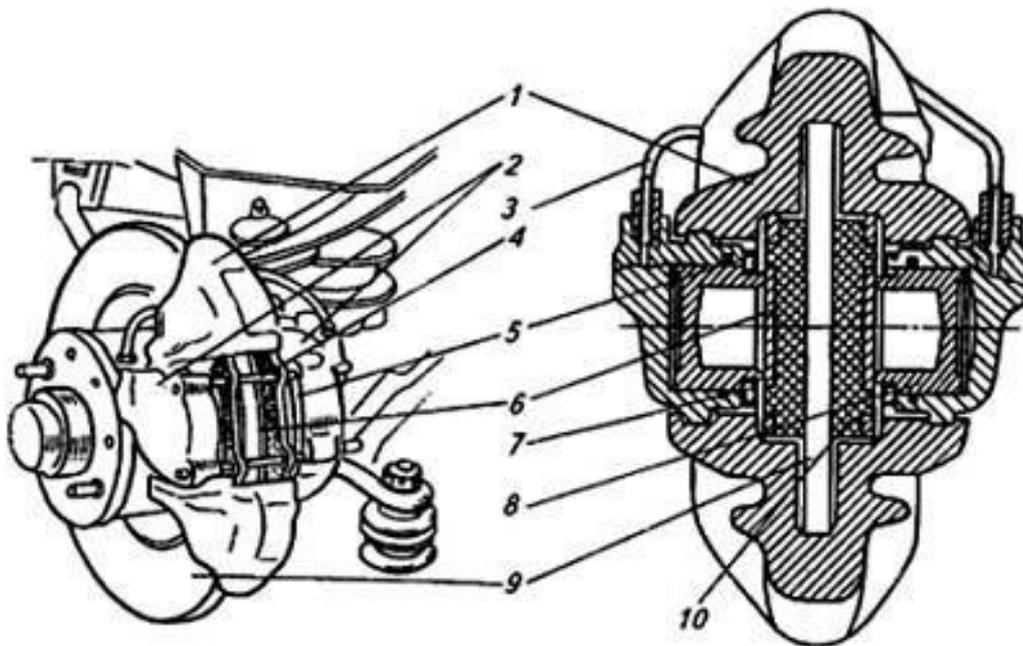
Дисковий гальмівний механізм з фіксованою скобою 1–скоба; 2–гальмівні циліндри; 3–трубопровід; 4–палець; 5–захисний чохол; 6–гальмівна колодка; 7–кільце ущільнювача; 8–поршень; 9–диск; 10–фрикційна накладка
